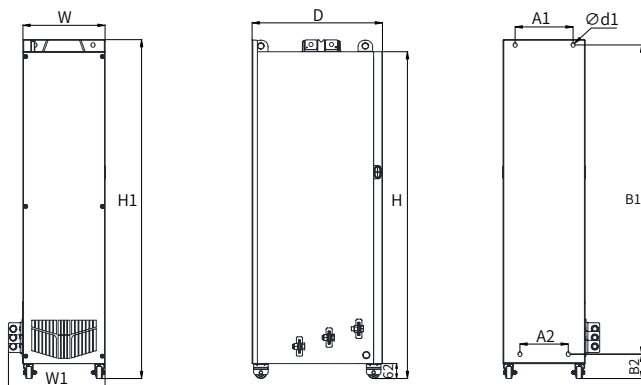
Габаритные и монтажные размеры конструкций Т10 - Т12 (без реакторов)
